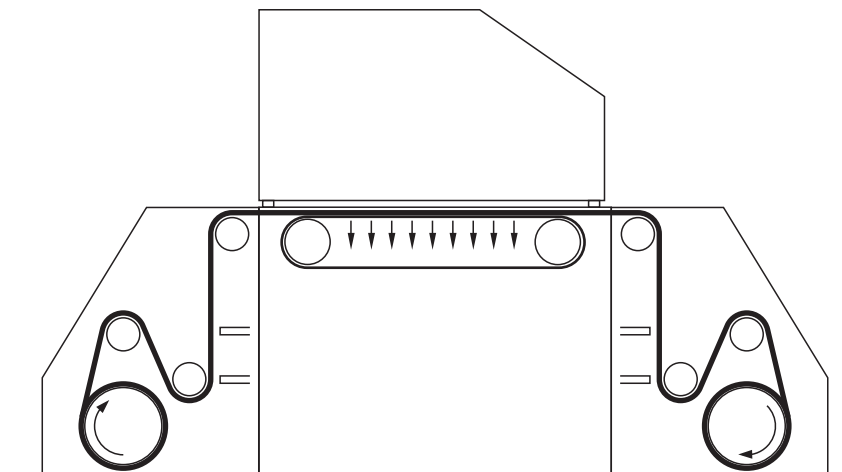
Проведение рулонного носителя через натяжной валик и направляющие ролики (здесь: схема для печати на лицевой стороне)
